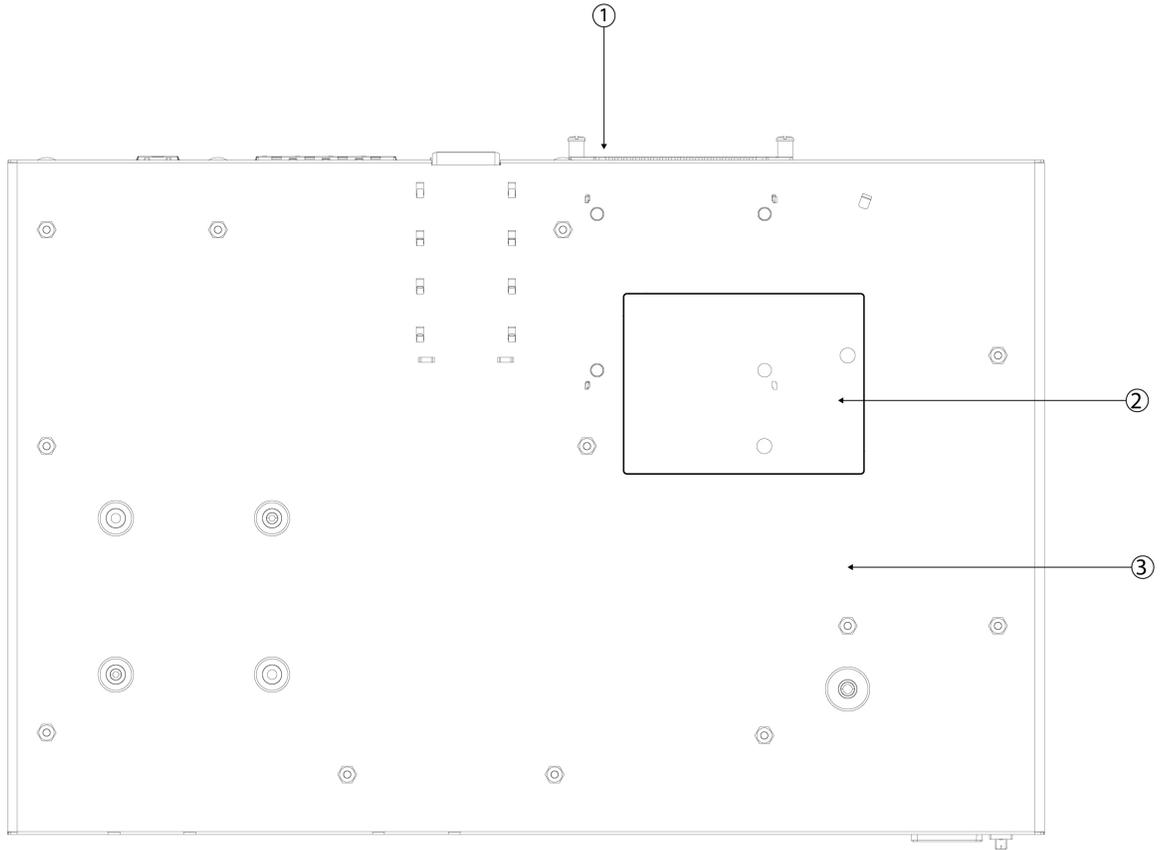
Tarjeta de recursos extraíble en el panel frontal del chasis
